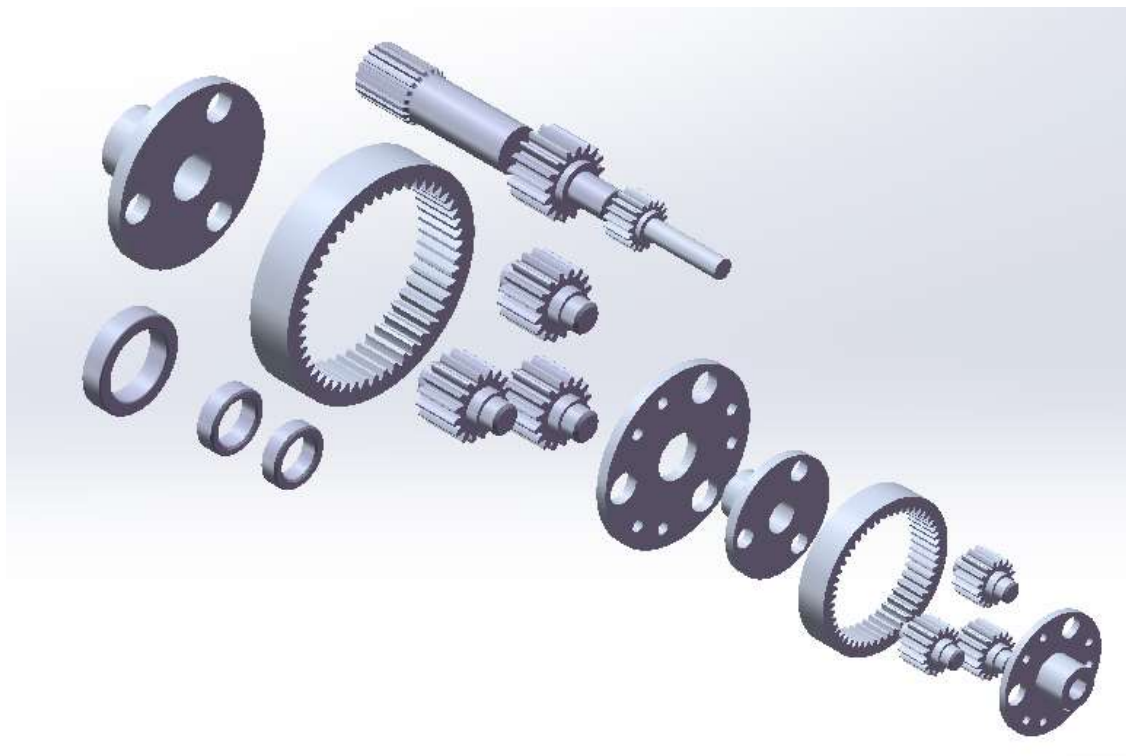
航空活塞发动机齿轮减速装置爆炸图
